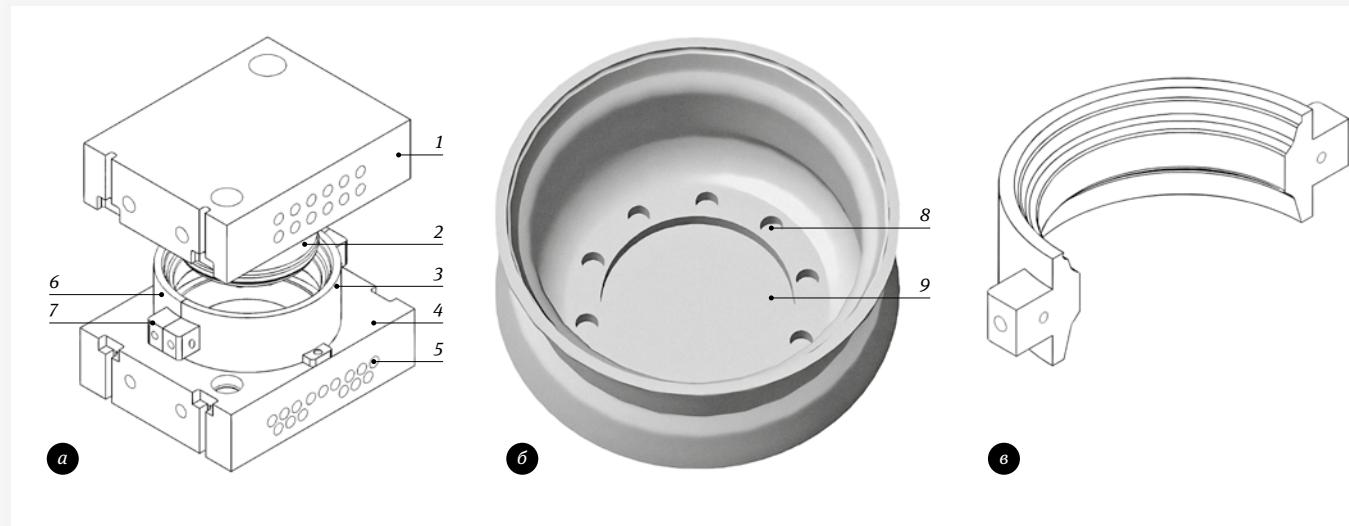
Штамп изотермической штамповки колесного диска из сплава AA6063, патент CN113941679A: а – общий вид (1 – держатель, 2 – пуансон, 3 – секторная матрица Б, 4 – матрицодержатель, 5 – отверстия для размещения нагревателей, 6 – секторная матрица А, 7 – зажимной элемент); б – штамповка детали «диск колесный» (8 – глухие отверстия, 9 – центральное глухое отверстие, формируемое при штамповке); в – секторная матрица А поз. 6 [17]
